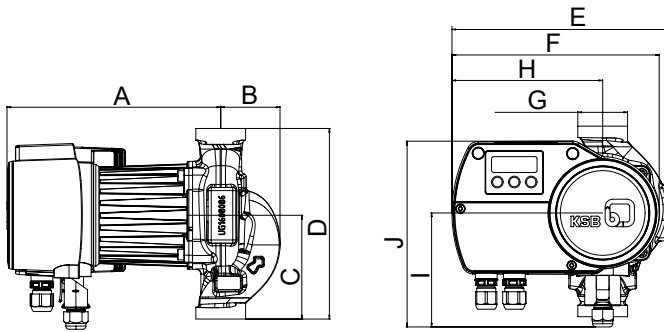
Pumpenaggregat mit Gewindeanschluss
